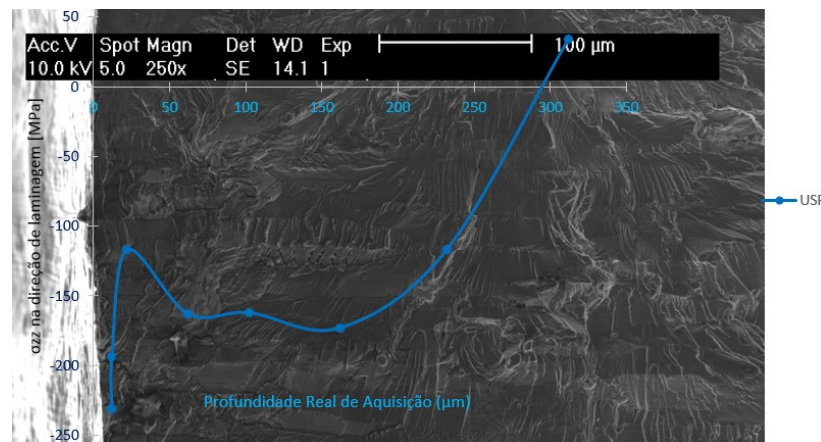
Sobreposição das tensões residuais USP e superfície de fratura (250x)
